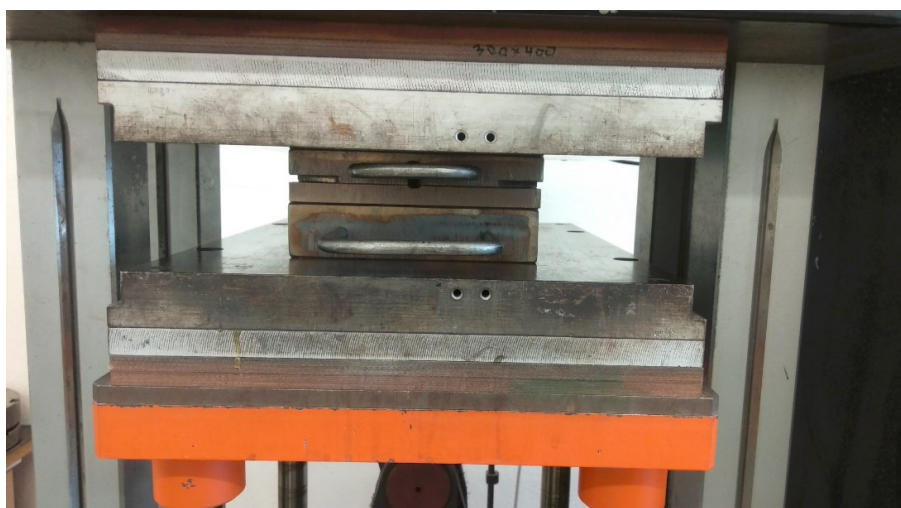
Použitý hydraulický vulkanizační lis IGTT
